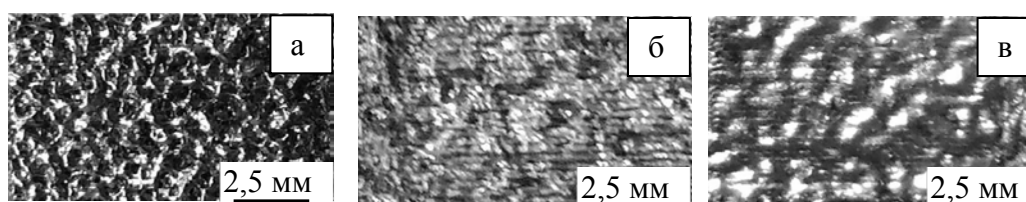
Фотографии образцов, полученных СЛС на установке «Луч»: а – образец №1, б – образец №2, в – образец №3
